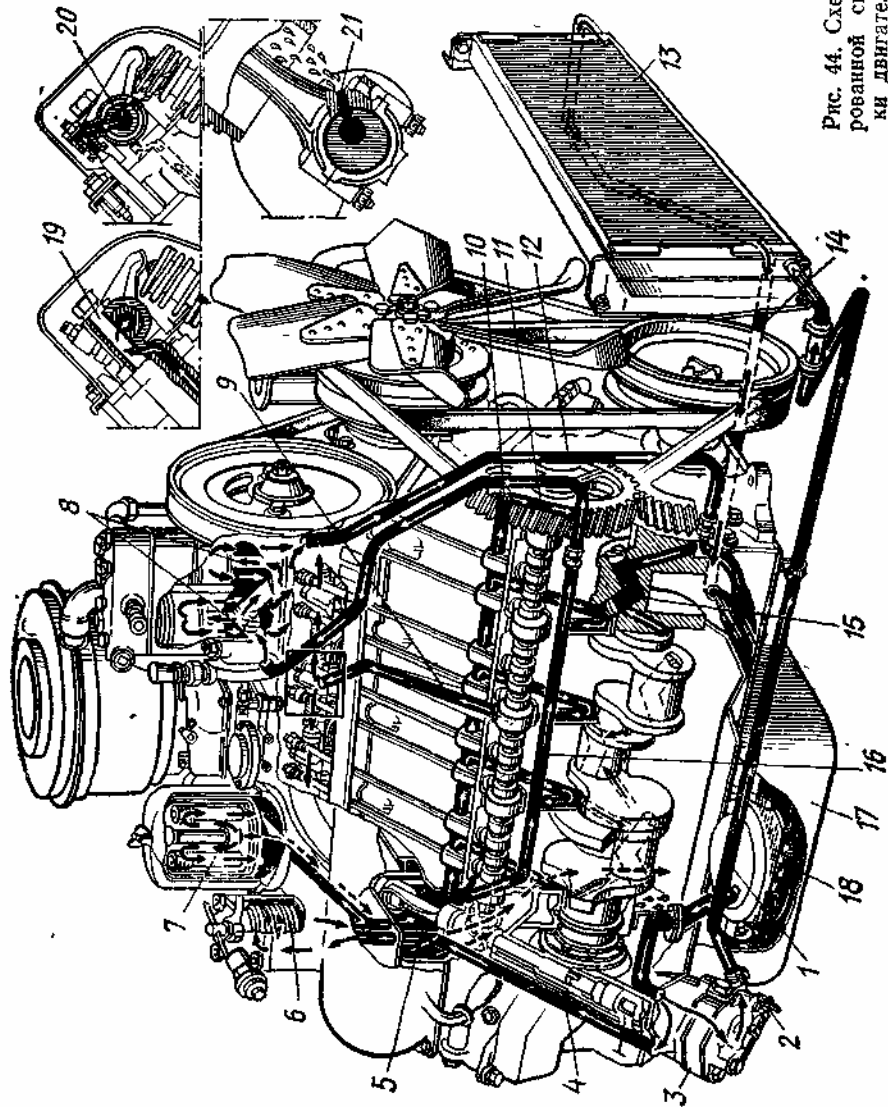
Схема комбинированной системы смазки двигателя ЗИЛ-130
